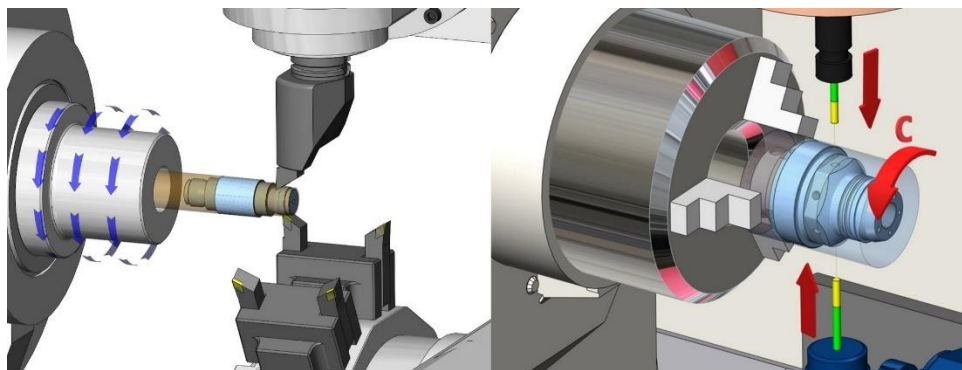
Синхронізування операцій на револьверній та фрезерній головках [18]
